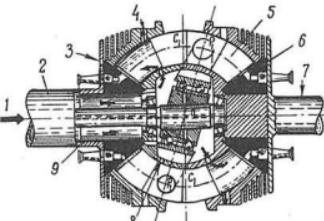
Продольный разрез двигателя 1 — впуск топлива; 2 — стационарный вал; 3 — ротор; 4 — выход отработавших газов из поршней; 5 — демонтируемая головка цилиндров; 6 — ведомый вал; 7 — ведущий вал; 8 — впускное отверстие; 9 — уплотнение.
